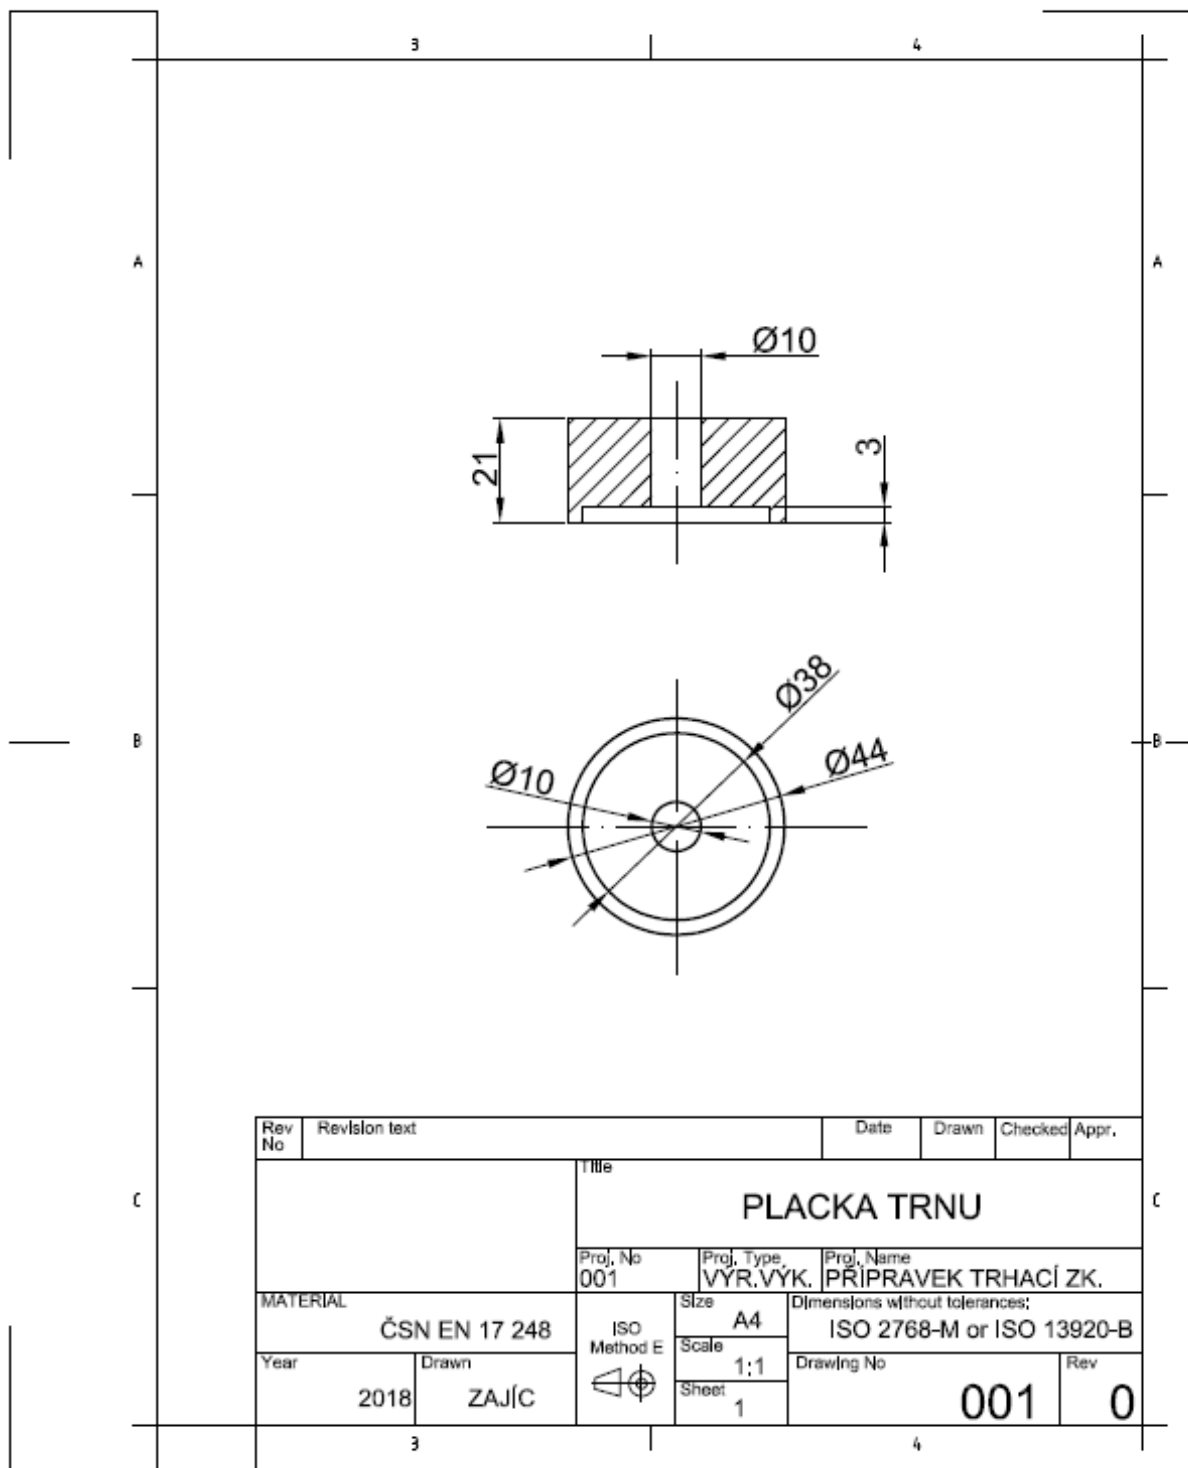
Technický výkres spodní základny upínacího přípravku
